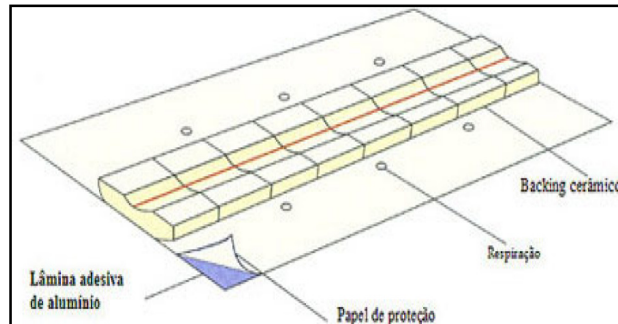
Fixação de suporte cerâmico na junta soldada com fita adesiva de alumínio
